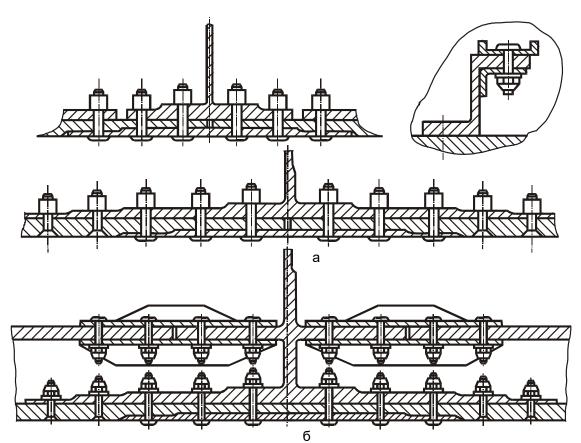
The design of the panel rearranging zones and the stringer set of the Yak-42: a - panel and wing; b - the first set of stringer
